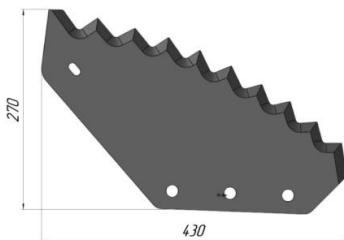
Внешний вид и габаритные размеры ножа шнека кормосмесителя-раздатчика АМКОДОР В-МИКС
